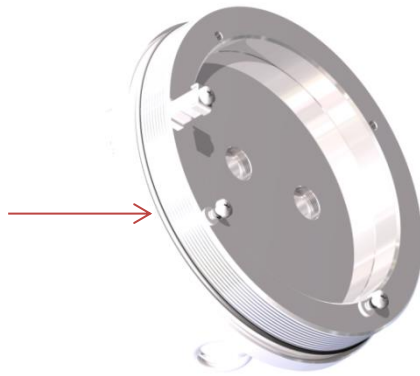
Posição da vedação de o-ringue de tipo T08-TNXCD
